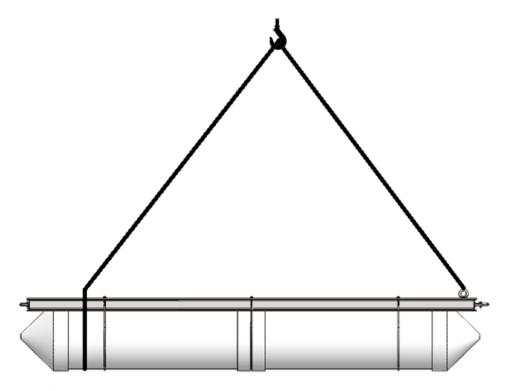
Vista lateral de elevación de sistema emplazamiento. Elaborado por los autores.
